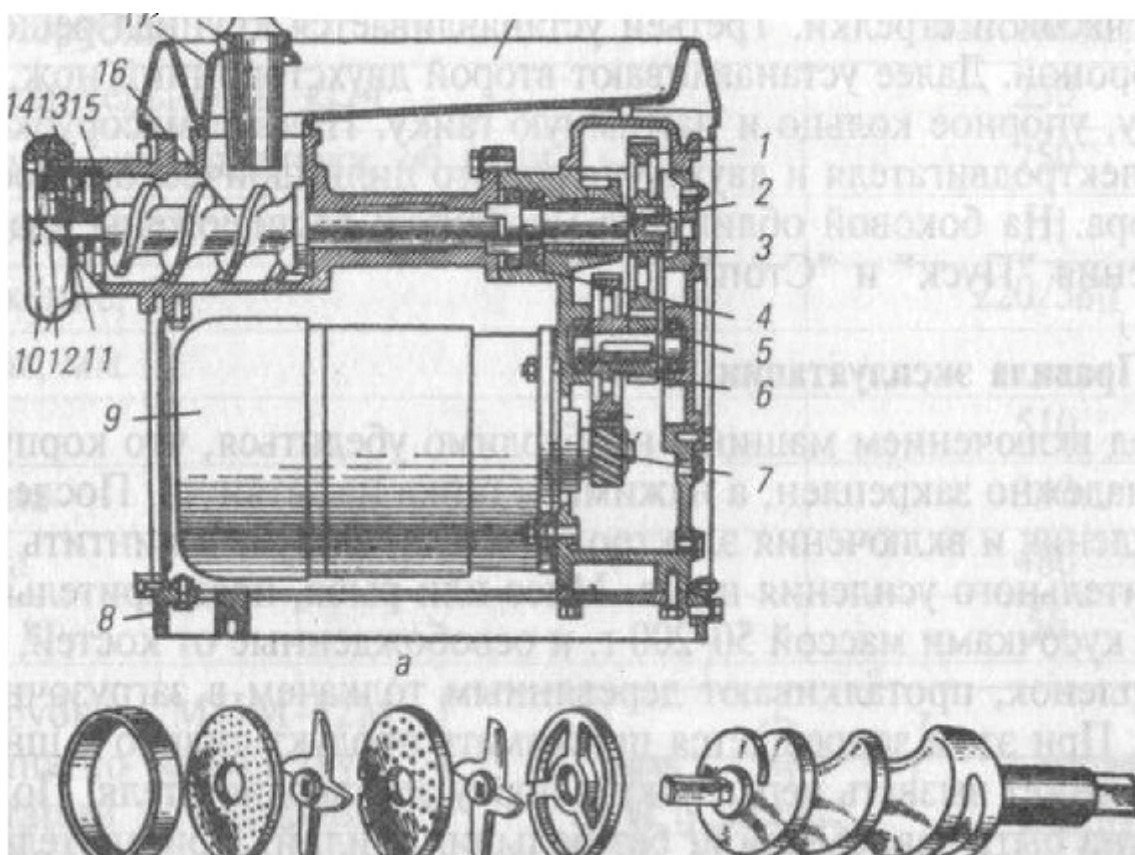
Мясорубка МИМ-82. а - разрез: 4,6 - зубчатые колеса; 2 - вал; 3 - шарикоподшипник; 4 - манжет; 5,7 - шестерни; 8 - основание; 9 - электродвигатель; 10 - зажимная гайка; 11,13 - ножевые решетки; 12 - упорное кольцо; 14 - двухсторонний нож; 15 - подрезная решетка; 16 - шнек; 17 - предохранитель; 18 - толкатель; 19 - загрузочная чаша; б - рабочие инструменты.
